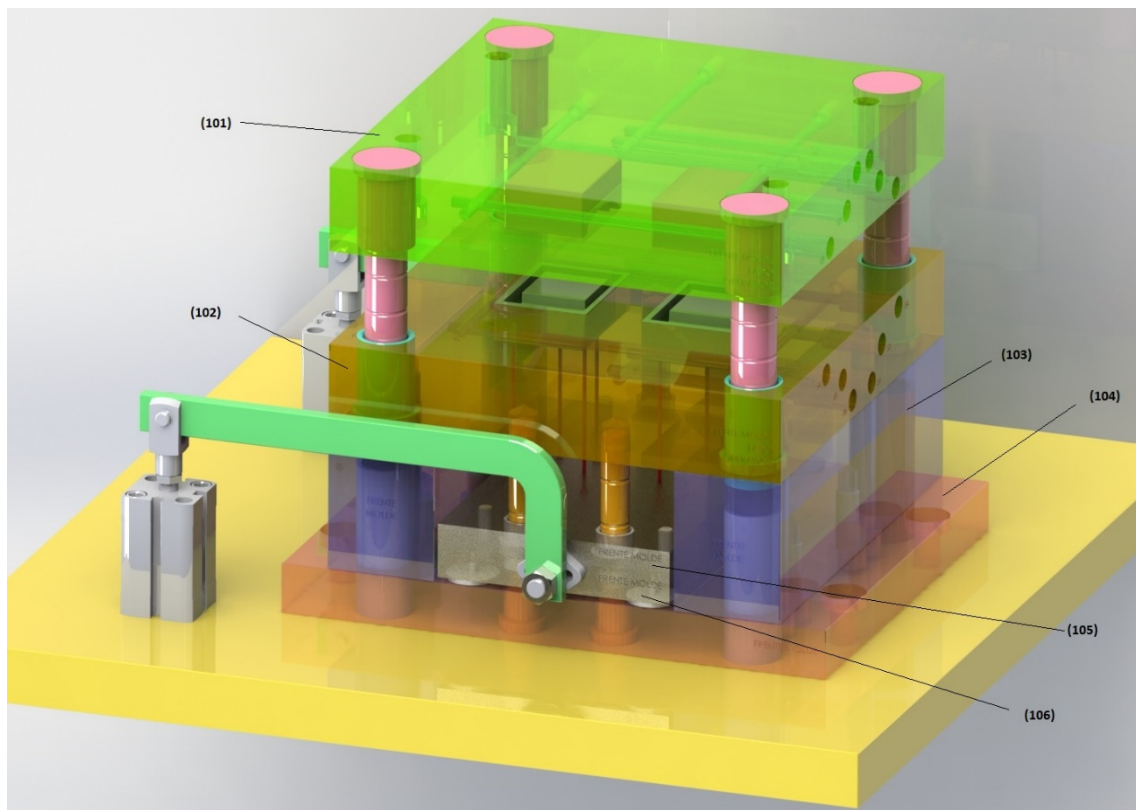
Molde de compressão (101) – Placa macho; (102) – Placa cavidade; (103) – Calço; (104) – Placa inferior de suporte; (105) – Placa de extração; (106) – Placa suporte de extração.
